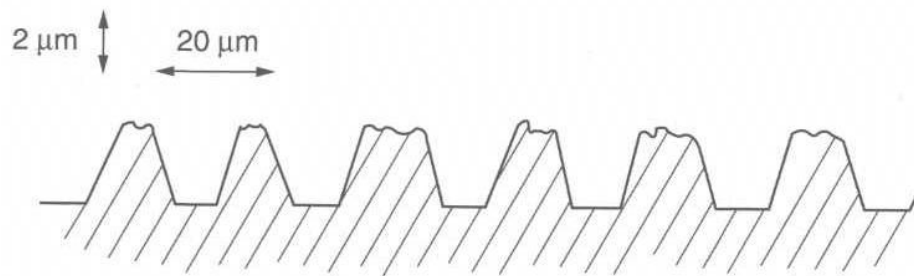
Aspect d'une surface métallique après usinage soigné, vue à fort grossissement (la hauteur des aspérités est exagérée par rapport à leur écartement).
